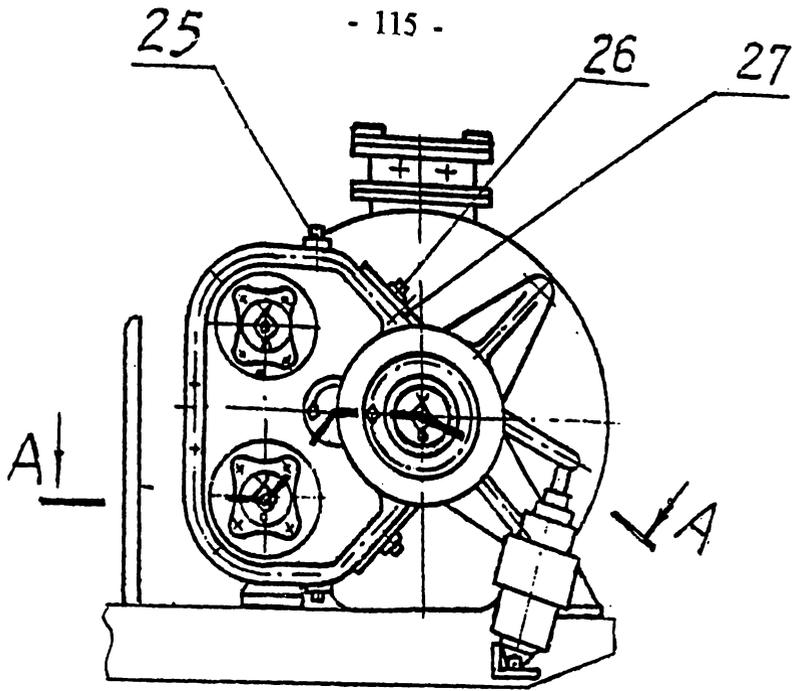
Редуктор привода ходовой части самоходного вагона
